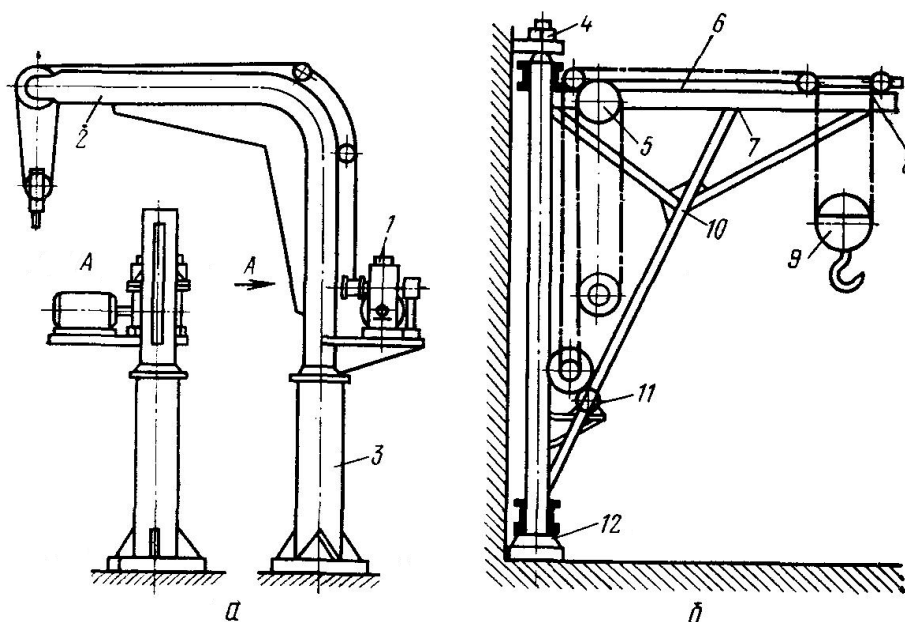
Схеми кранів поворотних: а - з нерухомою колоною, б - зі змінним вильотом; 1 - механізм підйому; 2 - стріла; 3 - колона; 4 - опори; 5 - механізм пересування; 6 - ланцюг; 7 - балка; 8 - візок; 9 - гак; 10 - укосина; 11 - механізм піднімальний
